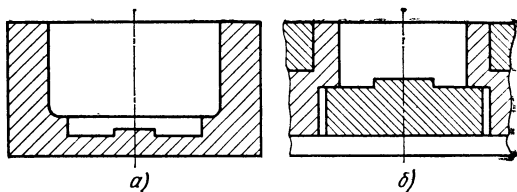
Конструкция цельных (а) и сборных (б) матриц пресс-формы.
